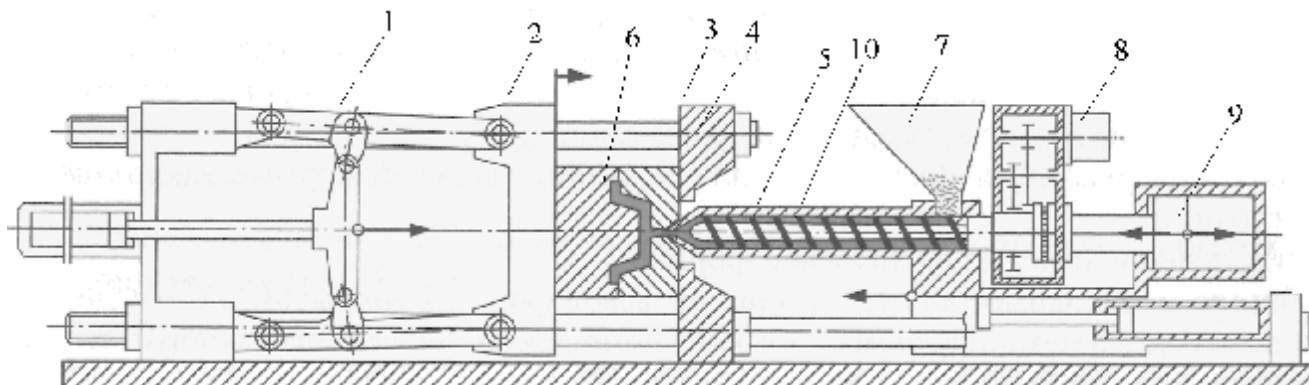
Схема литьевой машины с червячной пластикацией расплава: 1 – узел смыкания литьевой формы; 2, 3 – плиты, на которых закреплены полуформы для отливки изделий; 4 – пружины; 5 – инжекционный цилиндр; 6 – пресс-форма, состоящая из двух полуформ; 7 – бункер; 8 – механический привод; 9 – гидропривод; 10 – червяк; 11 – стержень, регулирующий перемещение гидроцилиндра путем воздействия на конечные выключатели.
